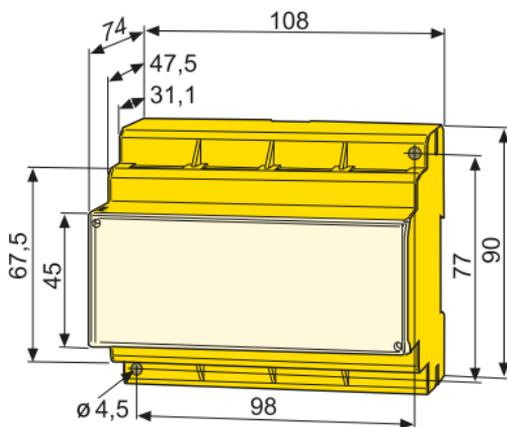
Disegno dimensionale, schema per montaggio con viti
